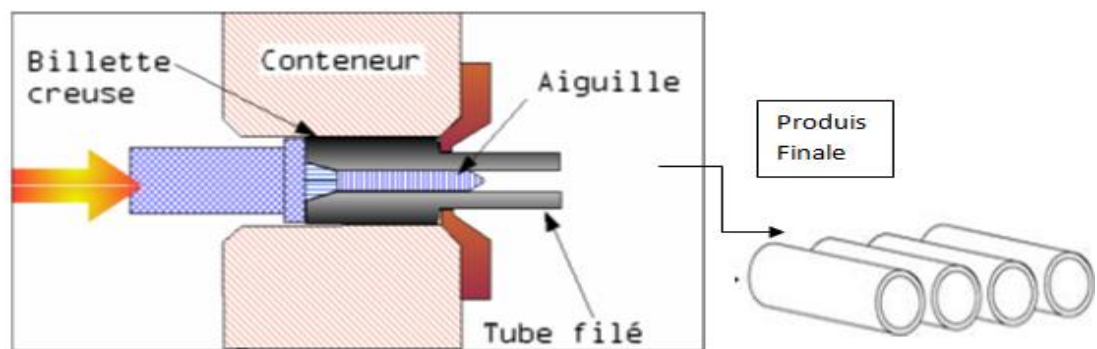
Fabrication de pipe sans soudure « Schéma du filage sur aiguille permettant d'obtenir un tube sans soudure » [7]
